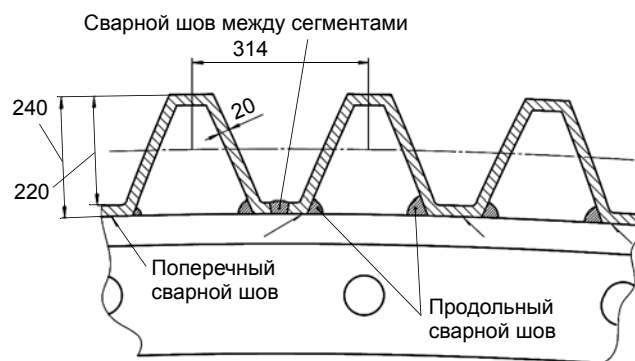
Схема закрепления гнутого зубчатого профиля на корпусе венцовой шестерни с помощью сварки
